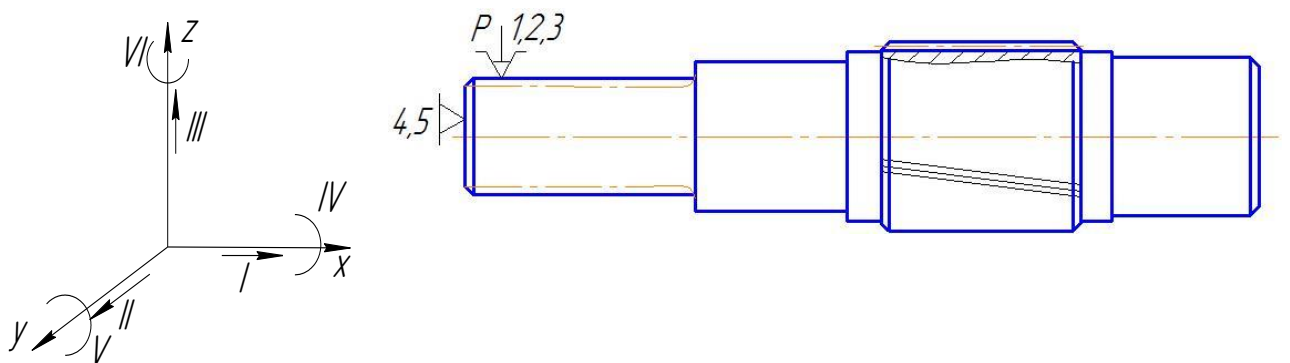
Ескіз обробки заготовки на операції 050
